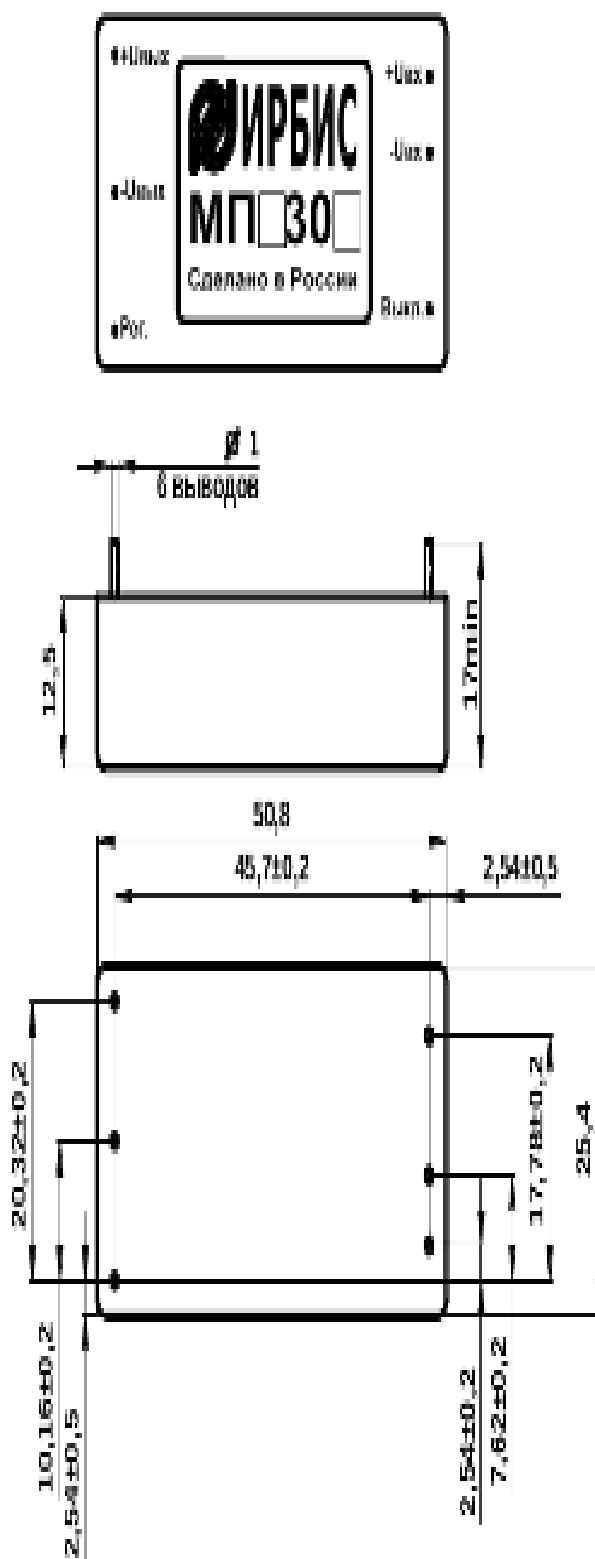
Габаритный чертеж модулей МПА(В,Е,Т)30
